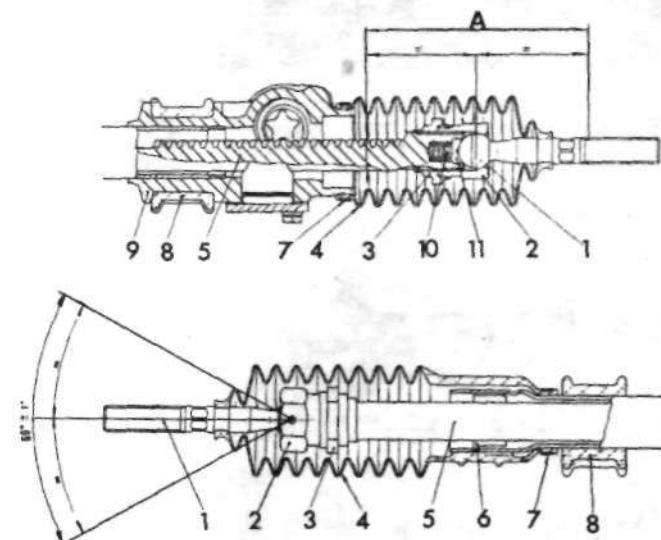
Сечение зубчатой рейки и шестерни (Раздел 6)
